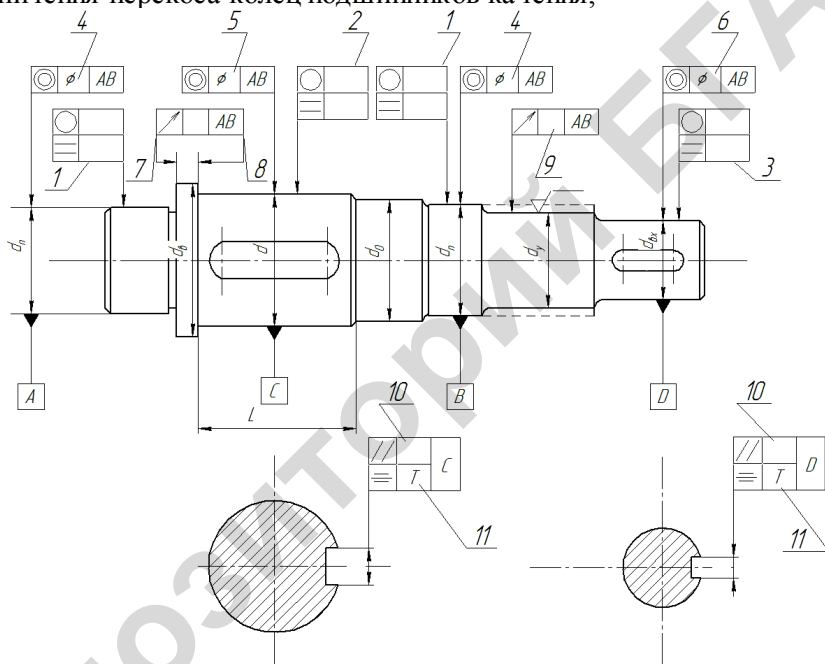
Пример нанесения размеров и условных обозначений
